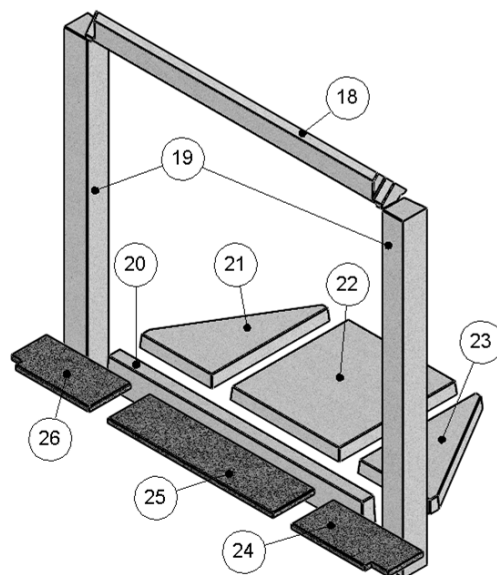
Installation pierres réfractaires en ciment du devant et du fond
